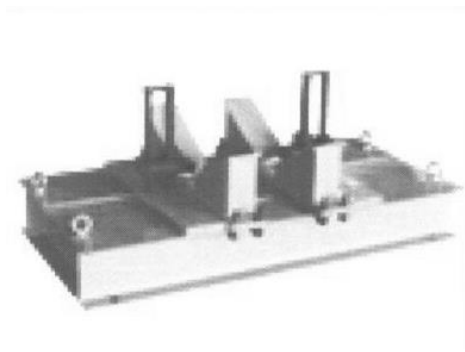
Установочное приспособление для арматуры с призмами
